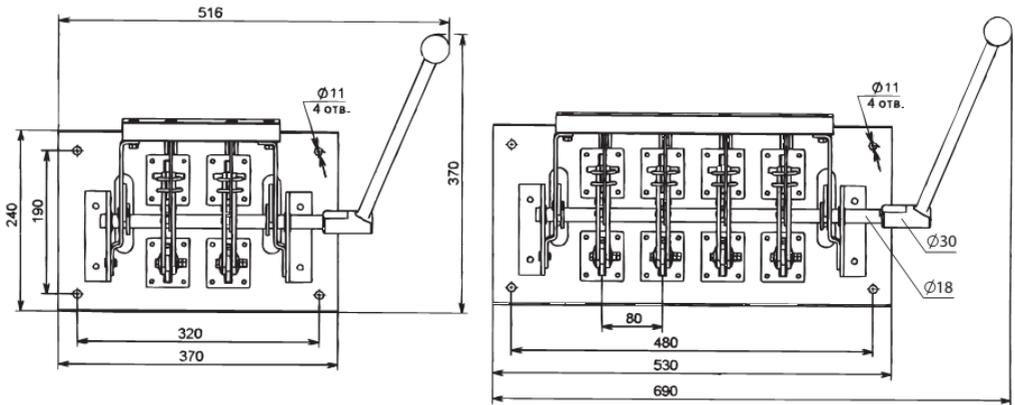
Разъединитель РЕ19 с боковой смещенной рукояткой РЕ19-44(45; 46)-31150-00 УХЛ3
